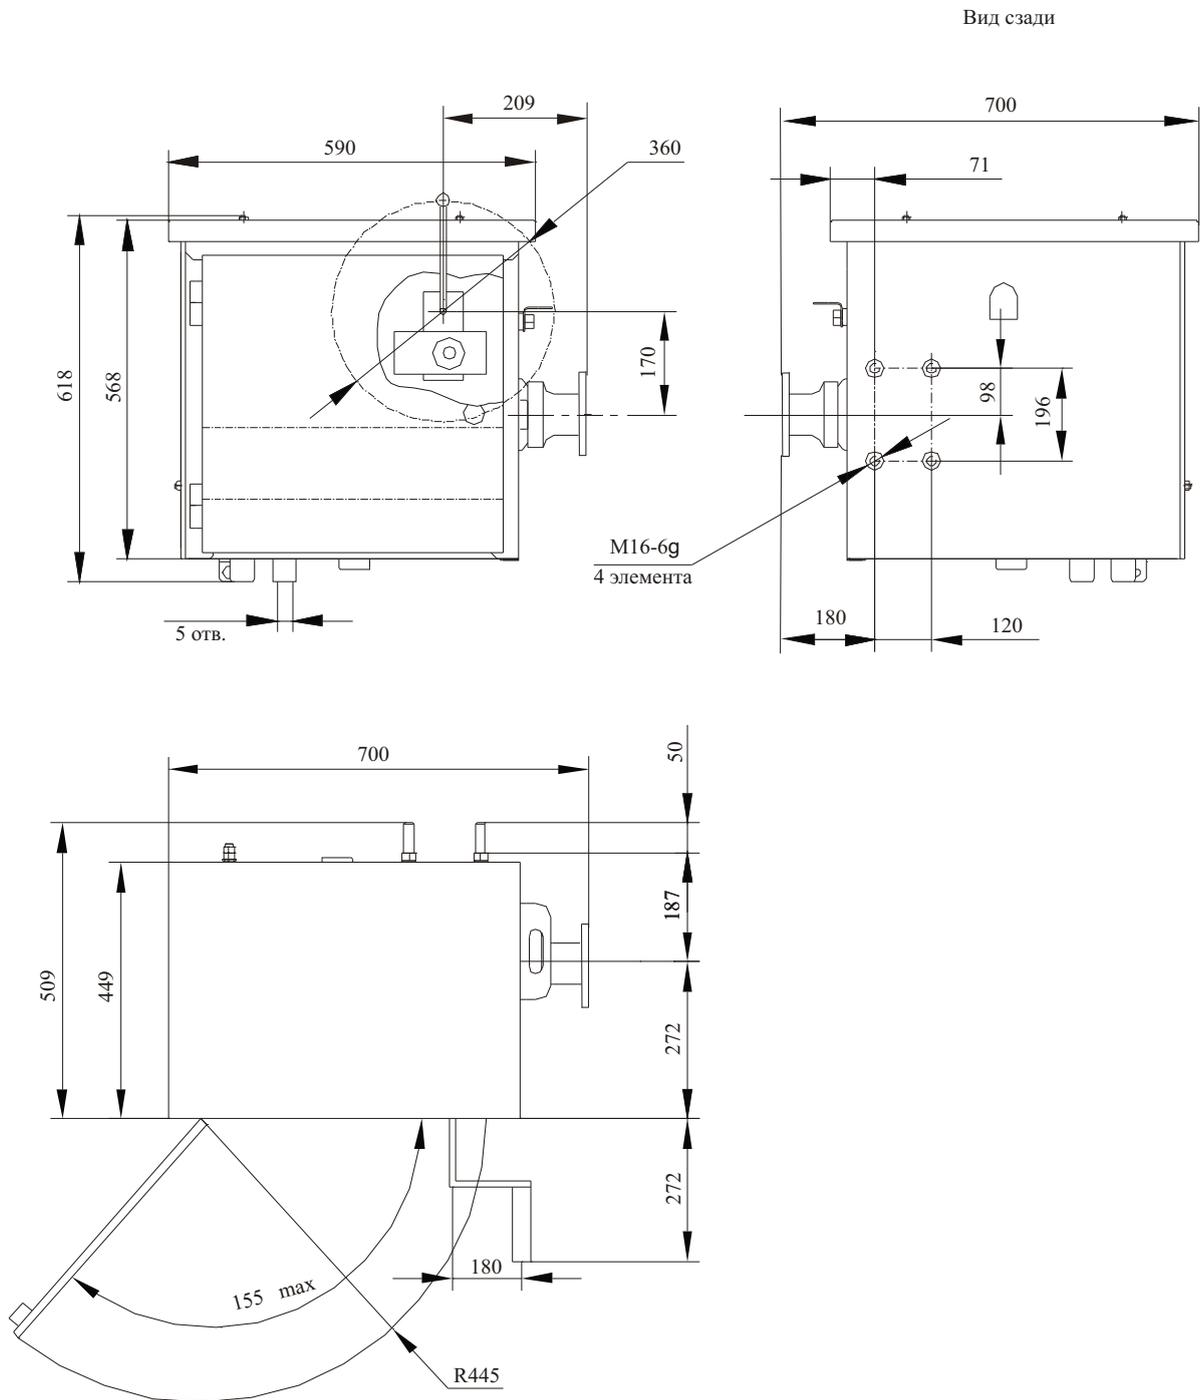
Приводы типоразмеров ПД-11-07УХЛ1, ПД-11-08УХЛ1
